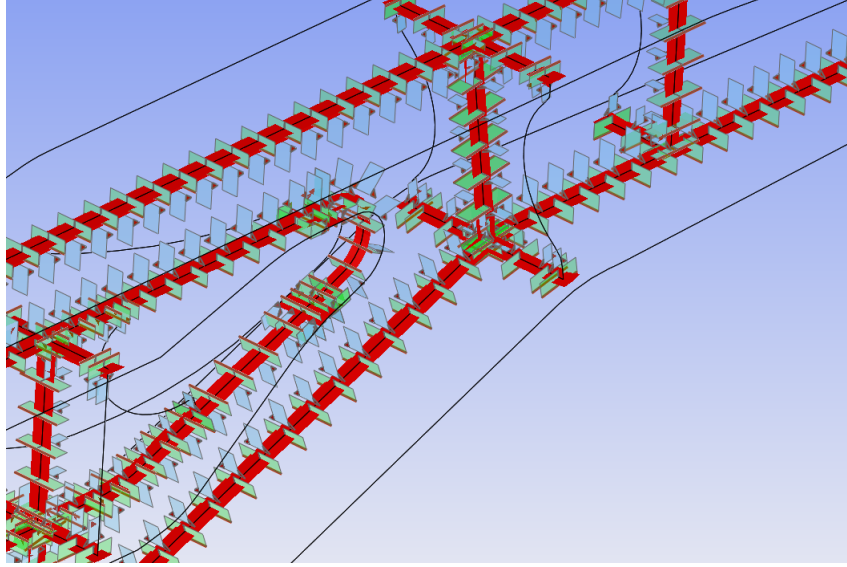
Model Üzerindeki Kaynak Dikiş Bölgeleri
